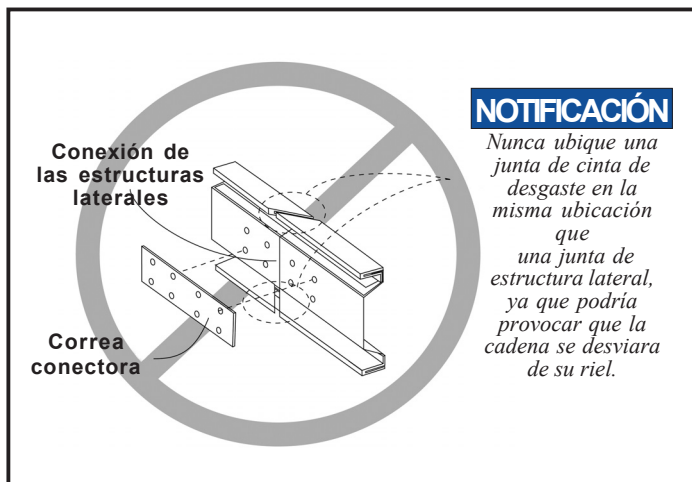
No ubique la junta de la cinta de desgaste en la junta de la sección de la cama
